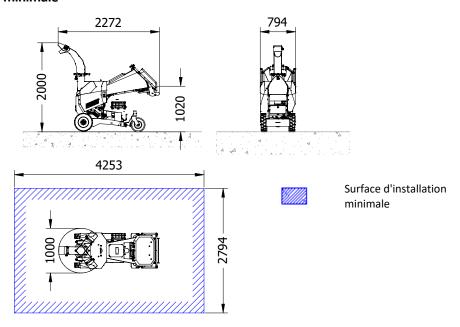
Surface d'installation minimale et dimensions de la machine
